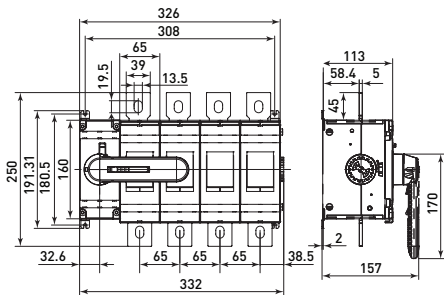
Габаритные и установочные размеры рубильников 630-800А 4Р
